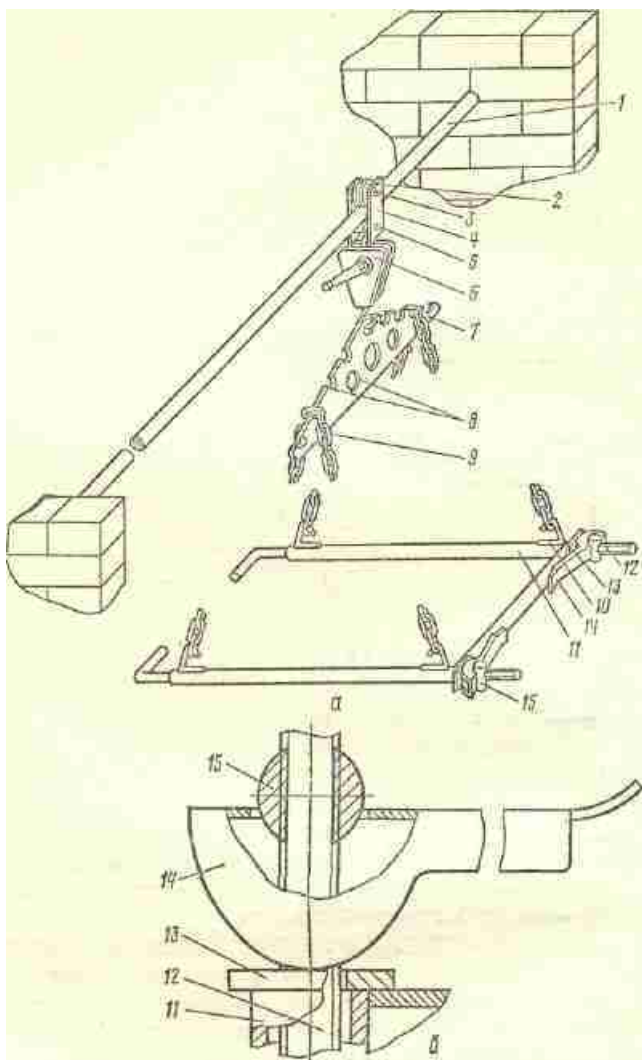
Приспособление для обслуживания ульев, расположенных в ряд:
